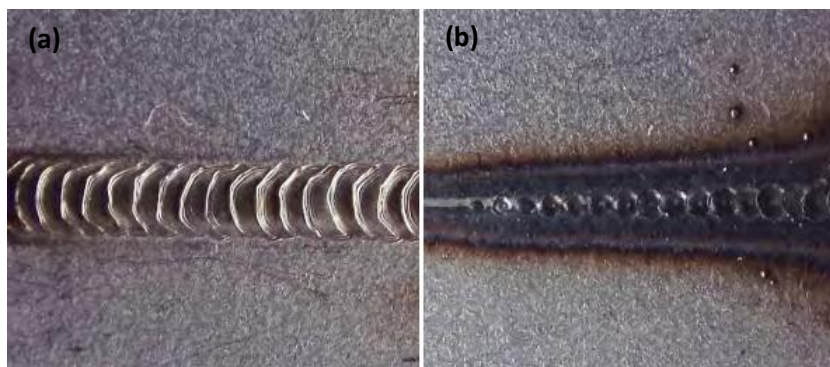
Soldadura laser (partes superior (a) e inferior (b)) sem a caixa
